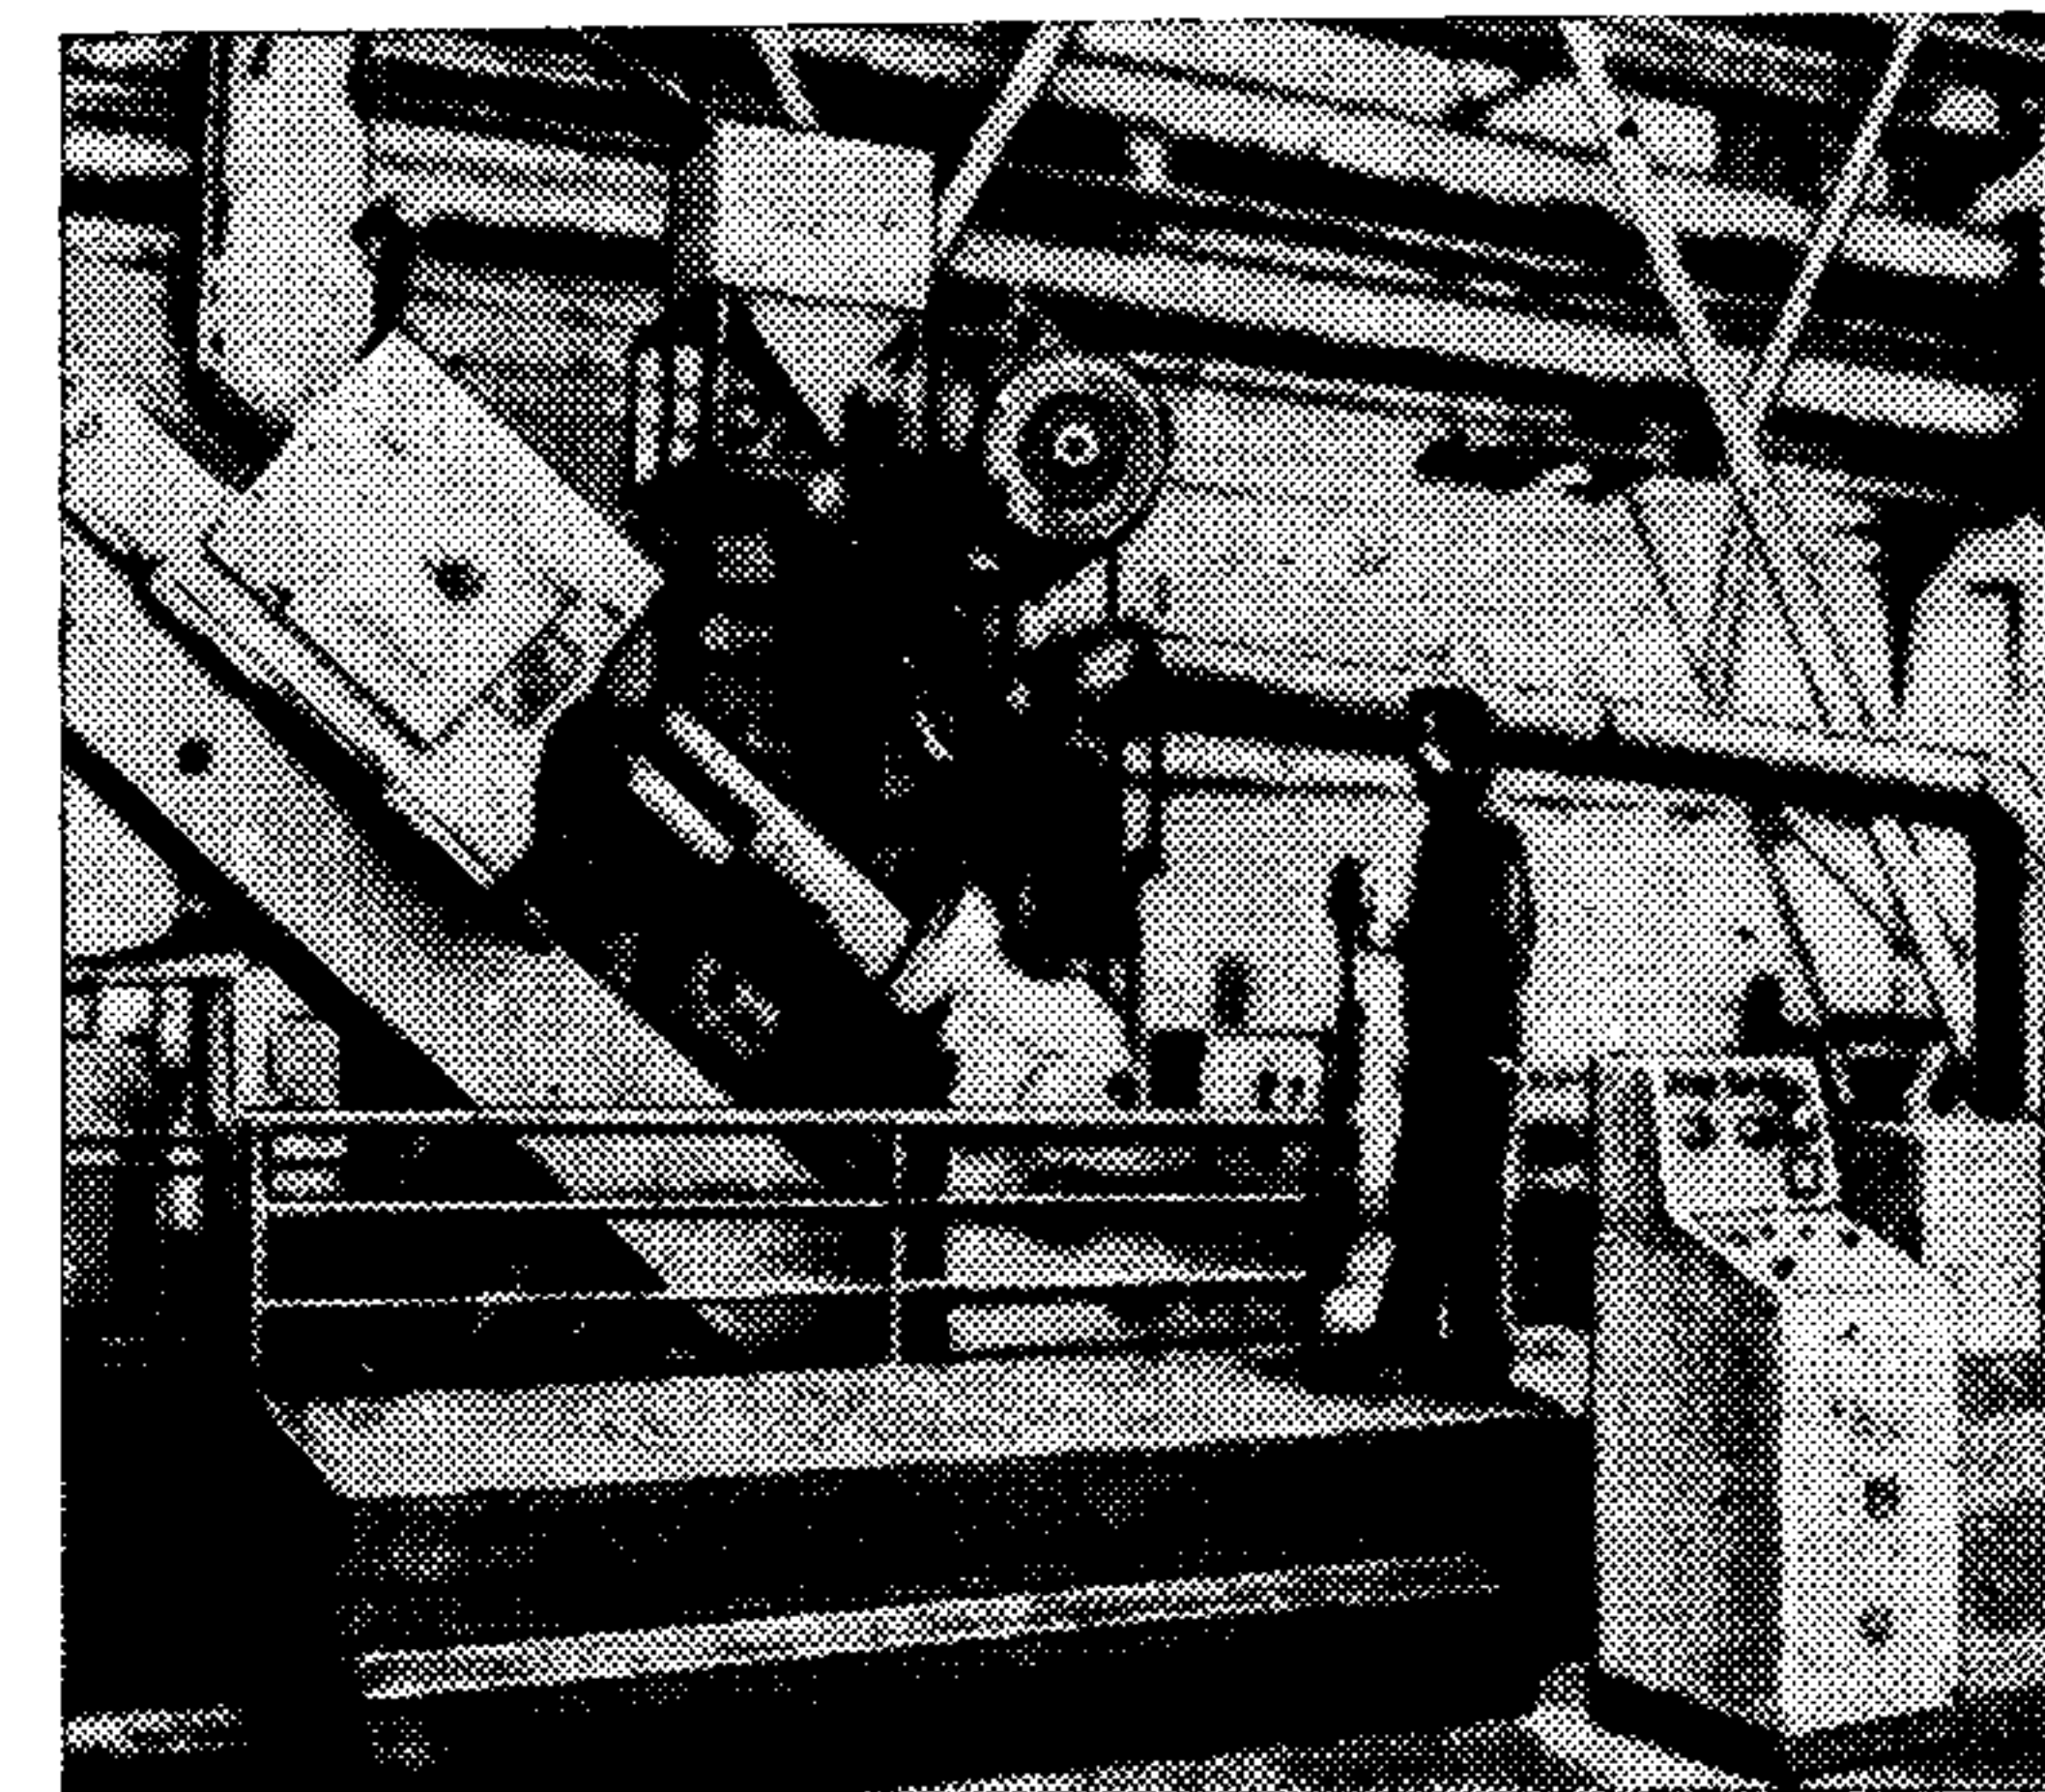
Устройство для автоматической наплавки прокатных валков с калибрами
